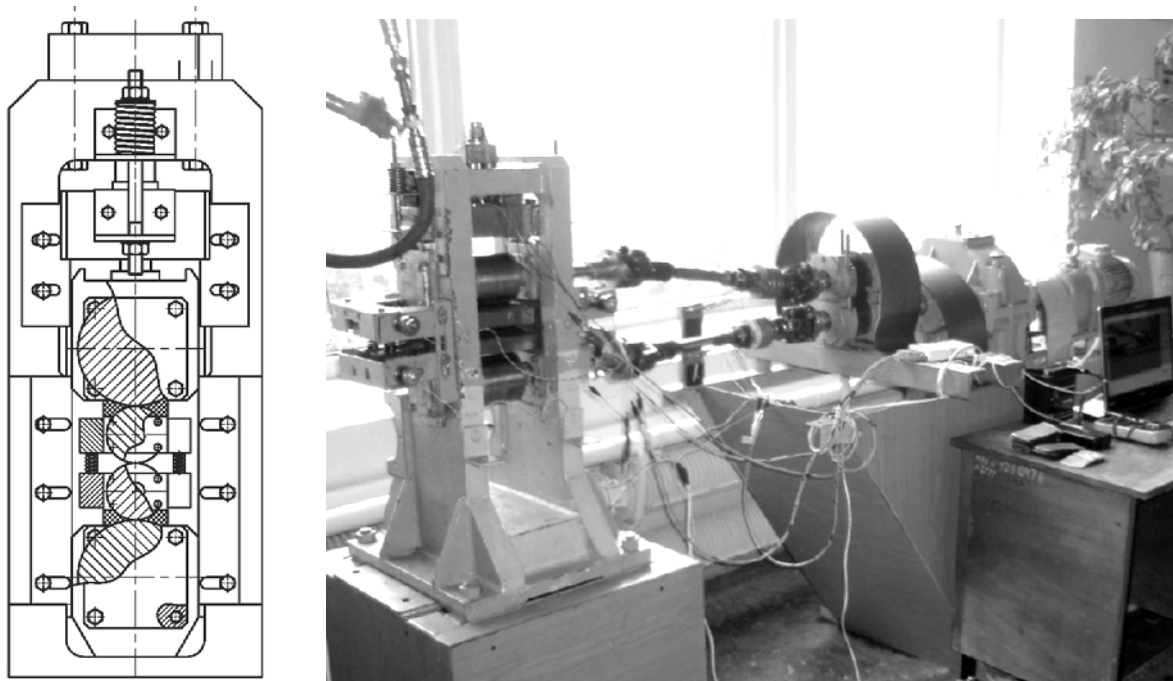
Внешний вид лабораторного стана 50/100 × 100 для исследования схемы привода на опорные валки кафедры АММ
